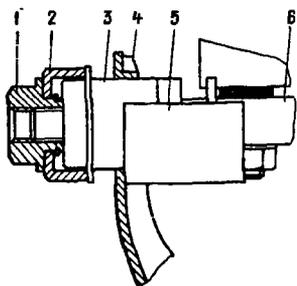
Схема запрессовки шарнира нижнего рычага с помощью приспособления 02.7823.9501: 1 - гайка; 2 - кольцо; 3 - шарнир; 4 - нижний рычаг; 5 - упор; 6 - ось нижнего рычага
